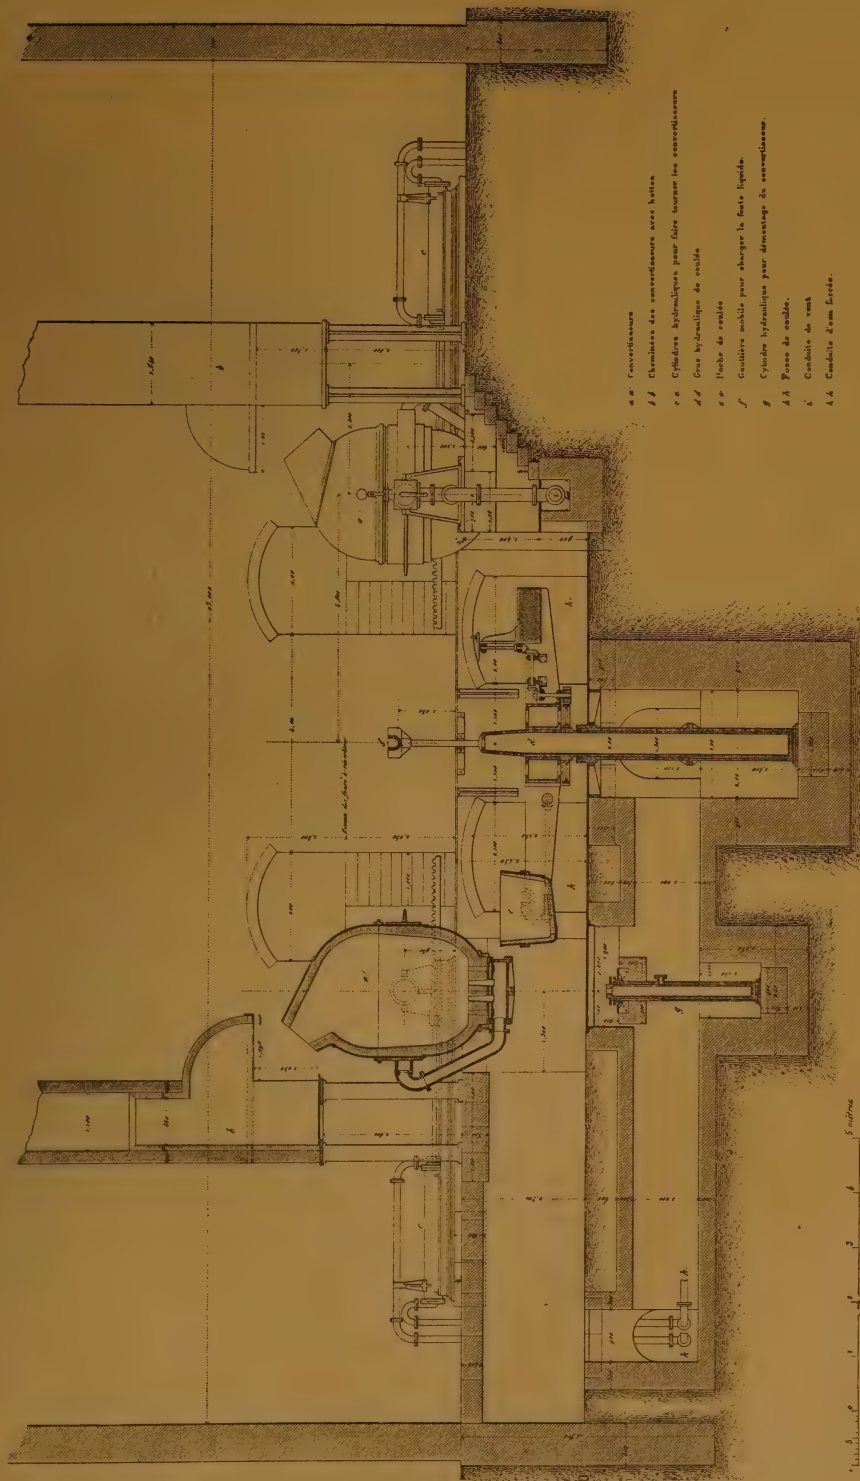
FABRICATION DE L'ACIER BESSEMER.
